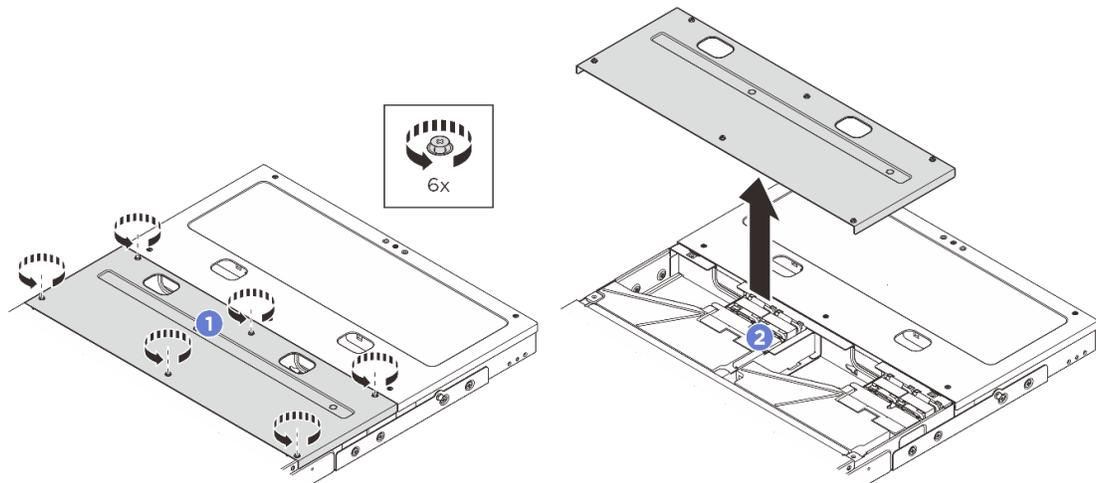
Extracción de la cubierta superior central del alojamiento 1U2N
